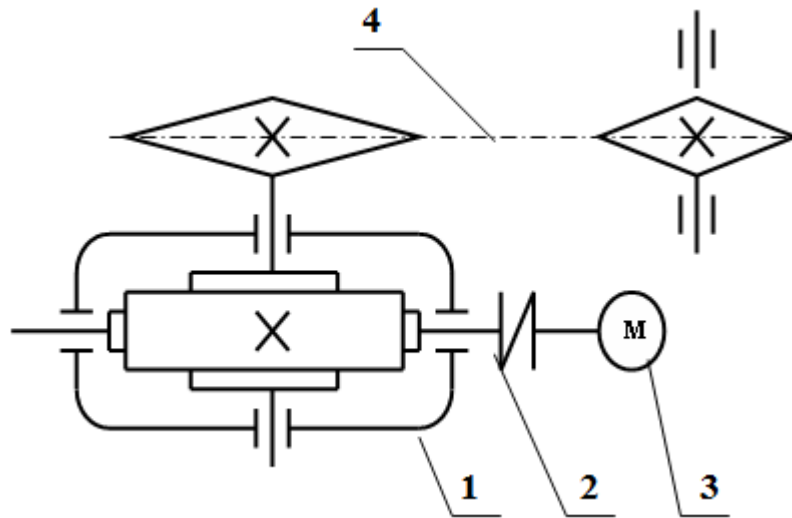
Привод поличного елеватора: 1 – електричний двигун, 2 – муфта типу МПВП, 3 – одноступінчатий черв'ячний редуктор з нижнім розташуванням черв'яка, 4 – ланцюгова передача.
